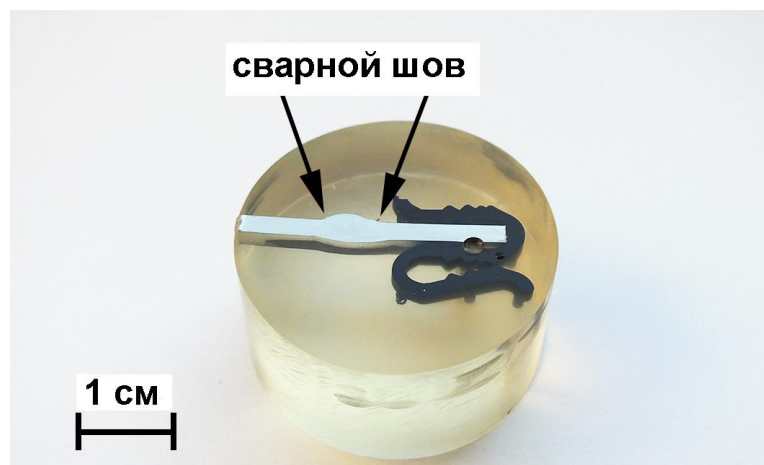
Фотография поперечного шлифа сварного соединения пластин из сплава алюминия 1579. Образец сделан для измерений методами SVET/SIET
